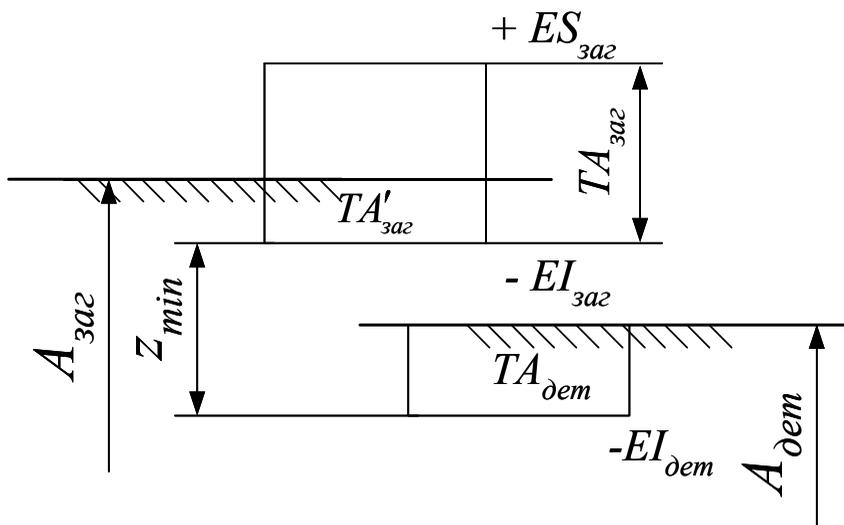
Расчетная схема для определения размера заготовки с учетом закона копирования погрешностей (охватываемый размер детали)
